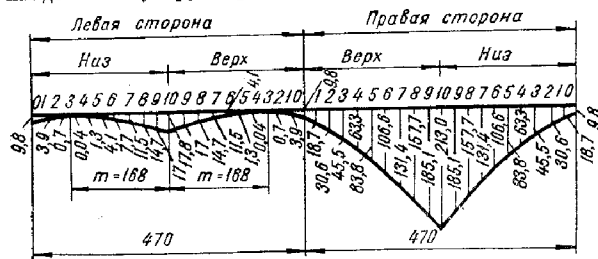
Развертка конца отростка сварного тройника.
